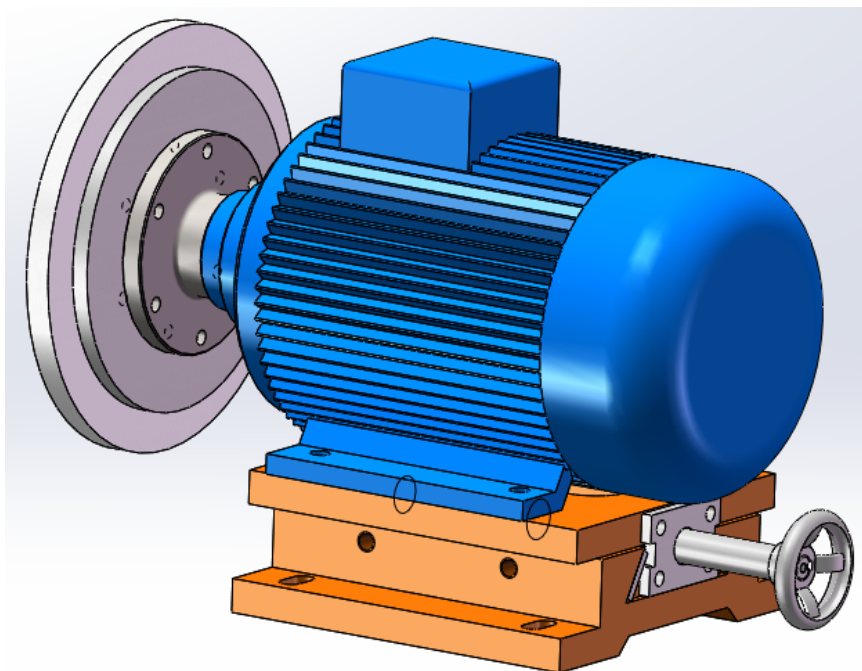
碟形磨边头 Figure 2-1 Disc squaring head
